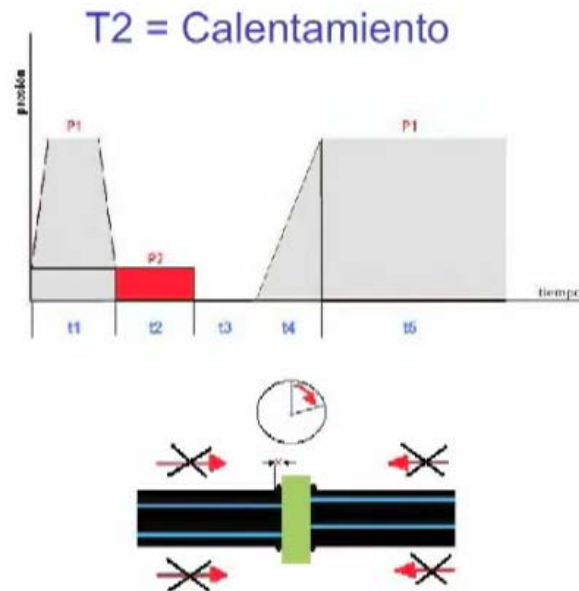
esquema del proceso de soldadura. Calentamiento.
